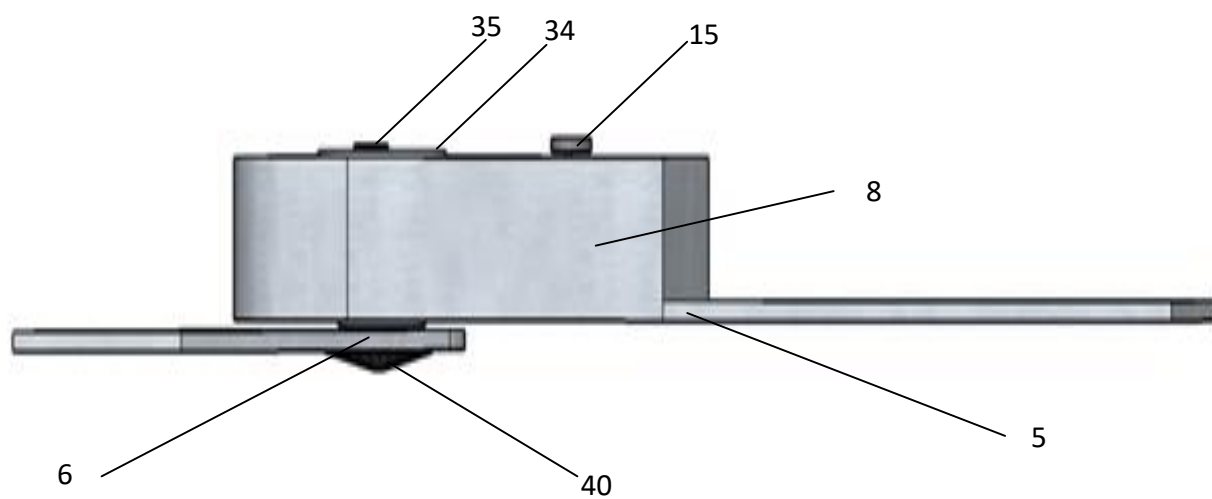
загальний вигляд збоку з'єднання коробчастого корпусу механізму редресації з шинами плеча та передпліччя
